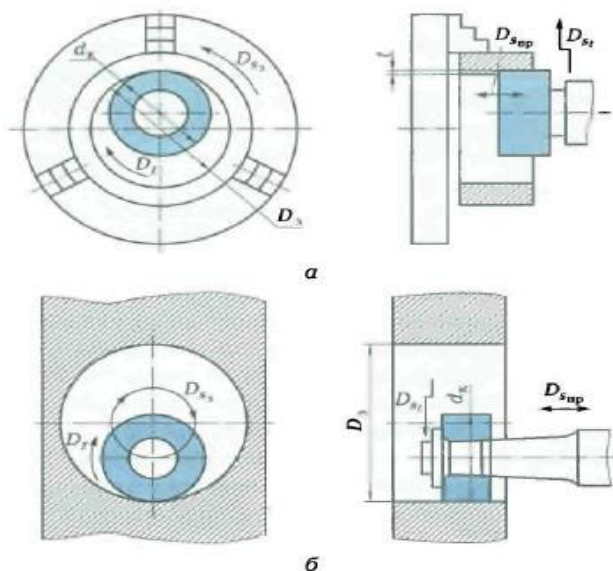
Схемы цилиндрического внутреннего шлифования:
